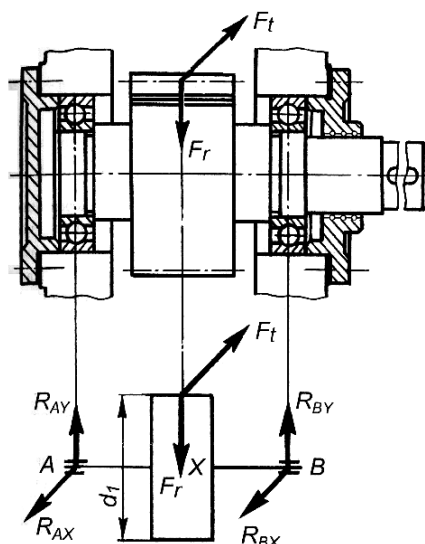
Подшипниковые узлы ведущего вала цилиндрического прямозубого редуктора
